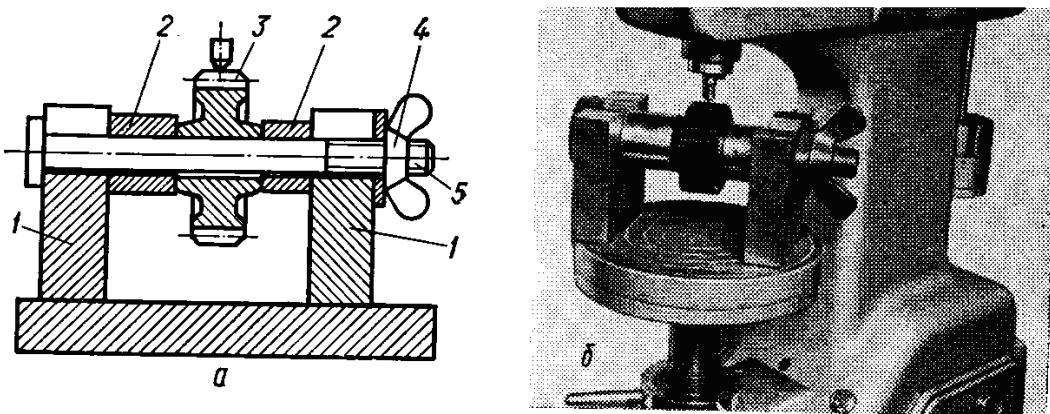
Приспособа для вимірювання твердості зірочок: а – схема приспособи; 1 – стойки; 2 – розпірні втулки; 3 – зірочка; 4 – гайка; 5 – гвінт; б – розположення приспособи на твердомірі Роквела.
